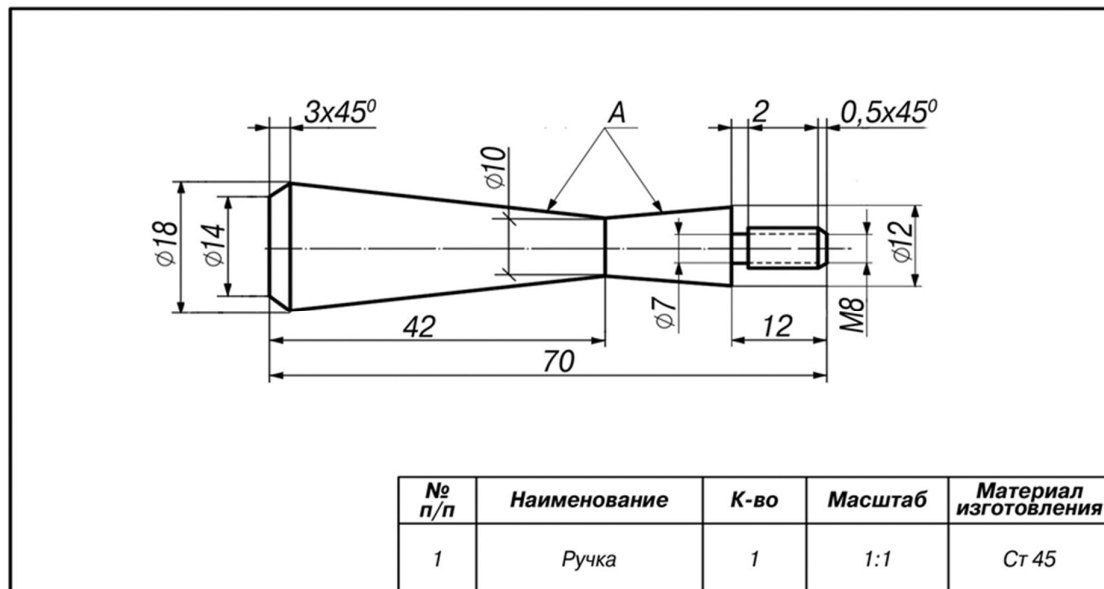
Ручка для токарно-винторезного станка ТВ 6
